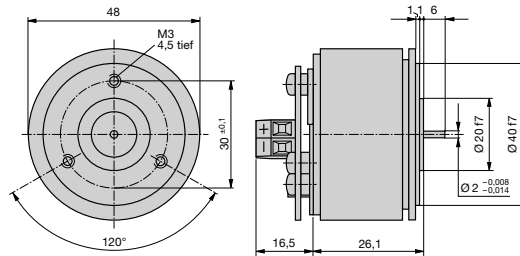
KINAX 2W2 mit Standard-Antriebswelle nur vorn, Ø 2 mm, Länge 6 mm. Anschlussvariante mit Schraubklemmen.
